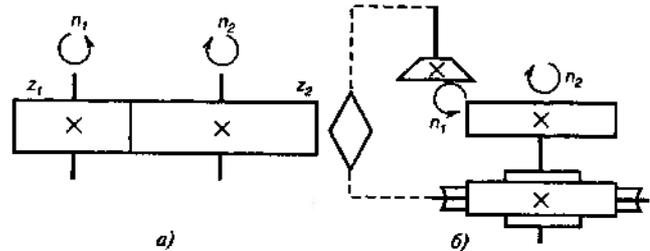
Обкат двох зубчастих коліс (а), інструменту і заготовки (б)
